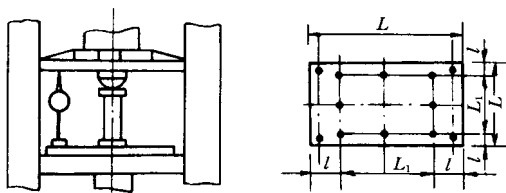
检验滑块下平面与工作台上平面的平行度
